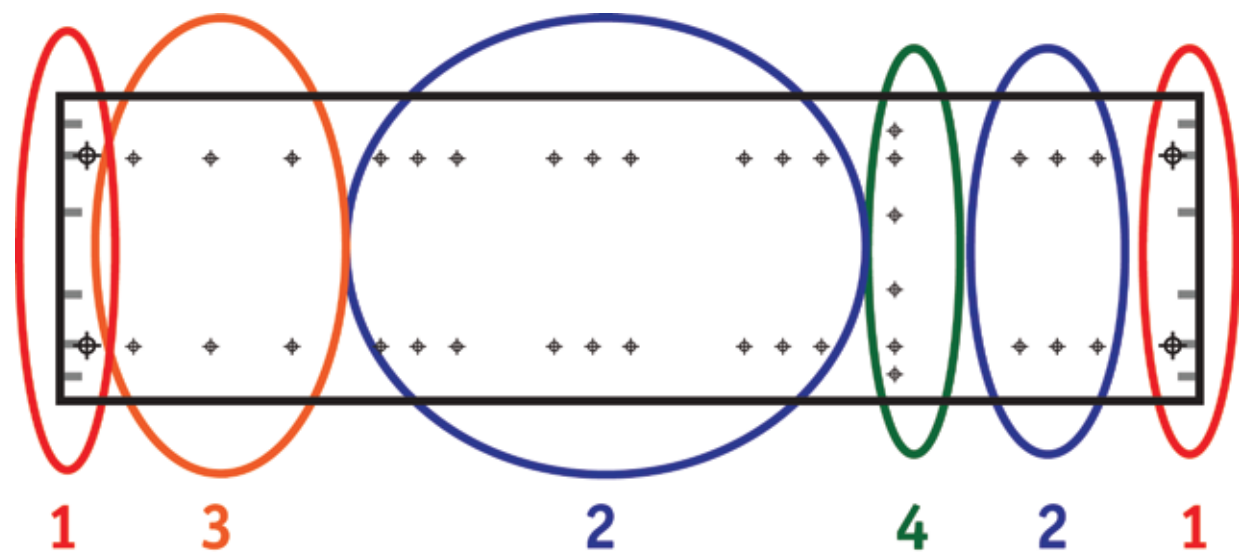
Пример расположения отверстий в детали корпусной мебели (боковая стенка шкафа):
